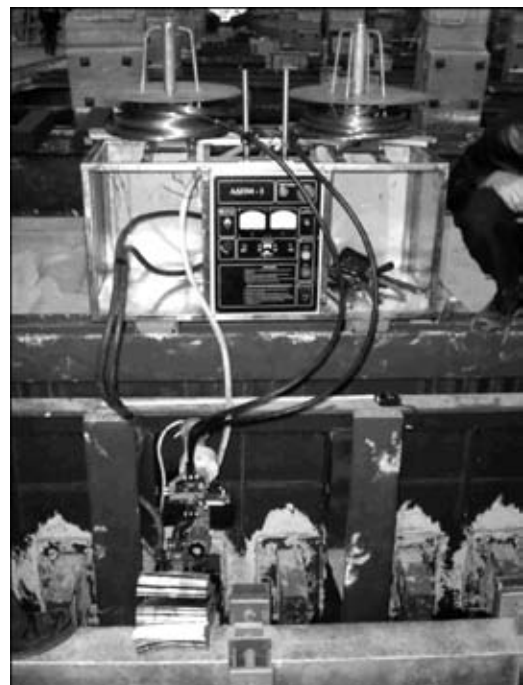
Аппарат АДПМ-2 для сварки соединения плата – блюмс при монтаже электролизера
